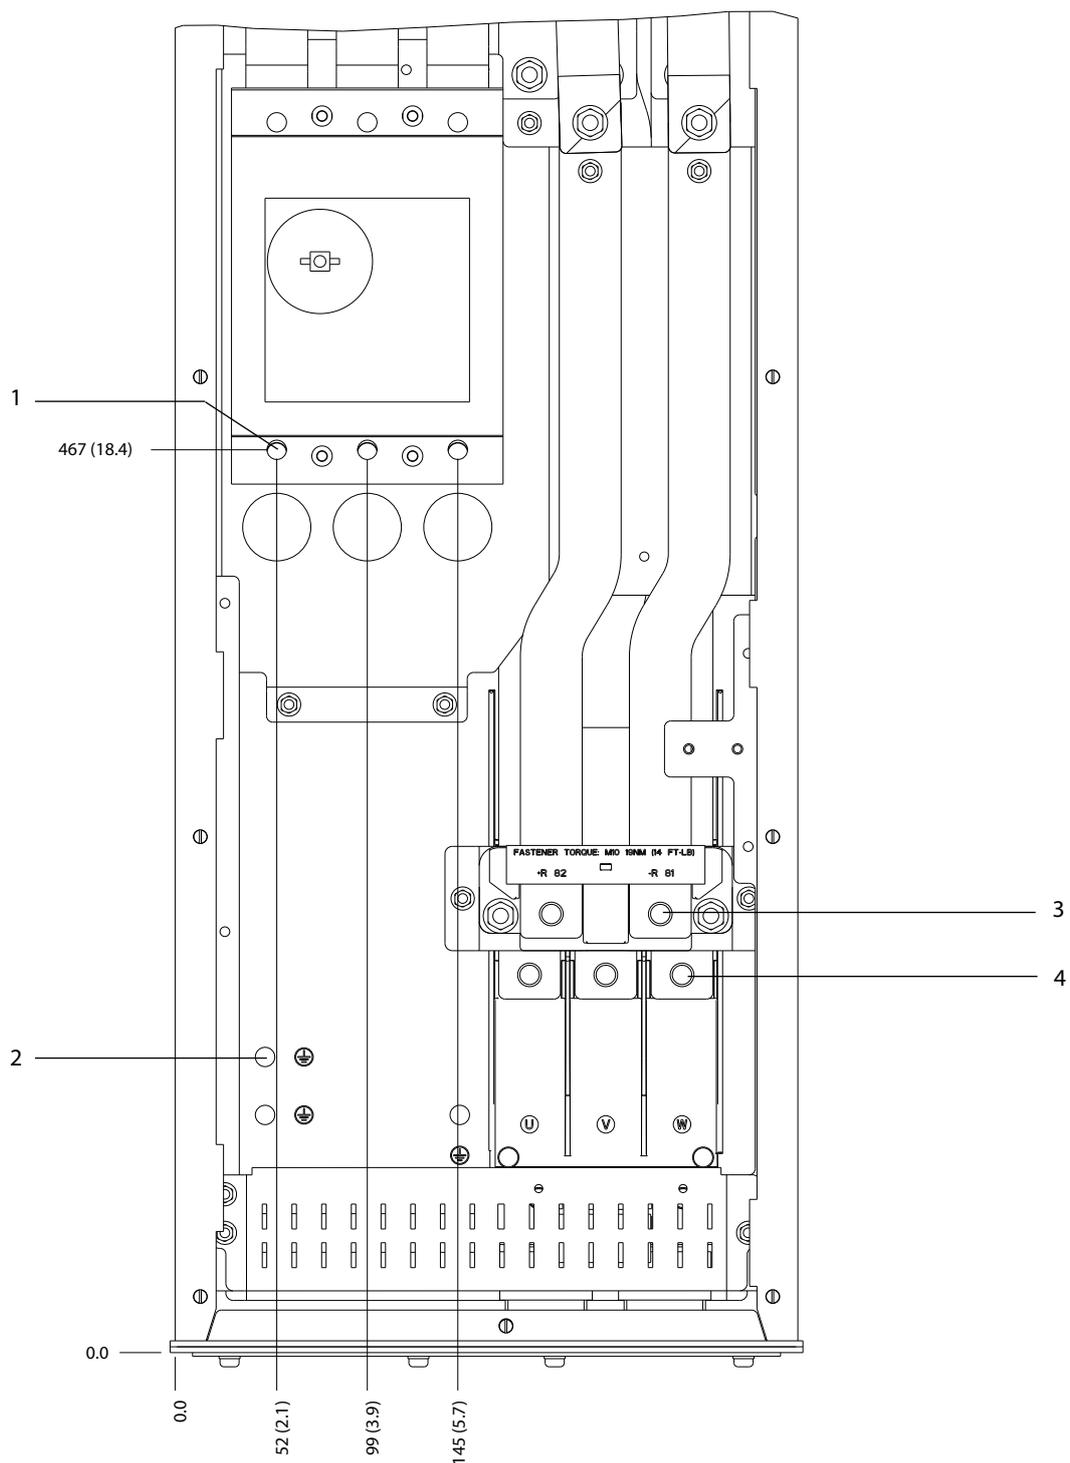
Dimensions des bornes D6h avec options contacteur et sectionneur (vue frontale)
